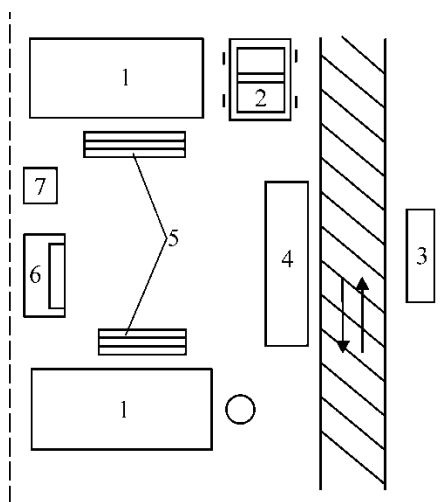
Робоче місце електро наплавлювальника (площа 16 м²): 1 – установка вібродугового наплавлення; 2 – стіл приймальний пересувний; 3 – ванна для флюсу; 4 – стелаж; 5 – тумбочка; 6 – урна для сміття; 7 – підставка-решітка
